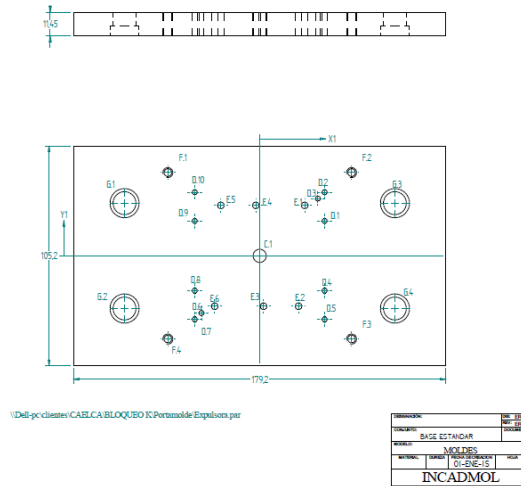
Tapa expulsora, molde de inyección. Autor Incadmol S.A.
